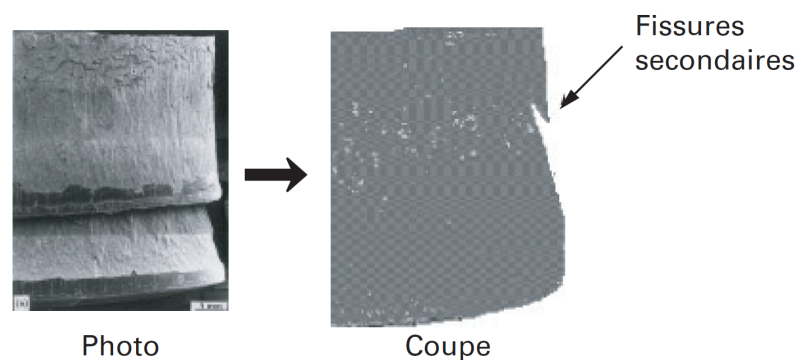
Exemple de fissures secondaires pour un acier (3,5 mm) [39]
